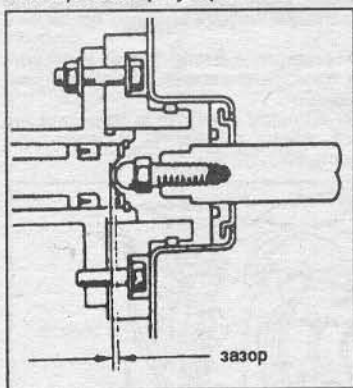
а К измерению зазора в паре толкатель усилителя/поршень главного тормозного цилиндра.
